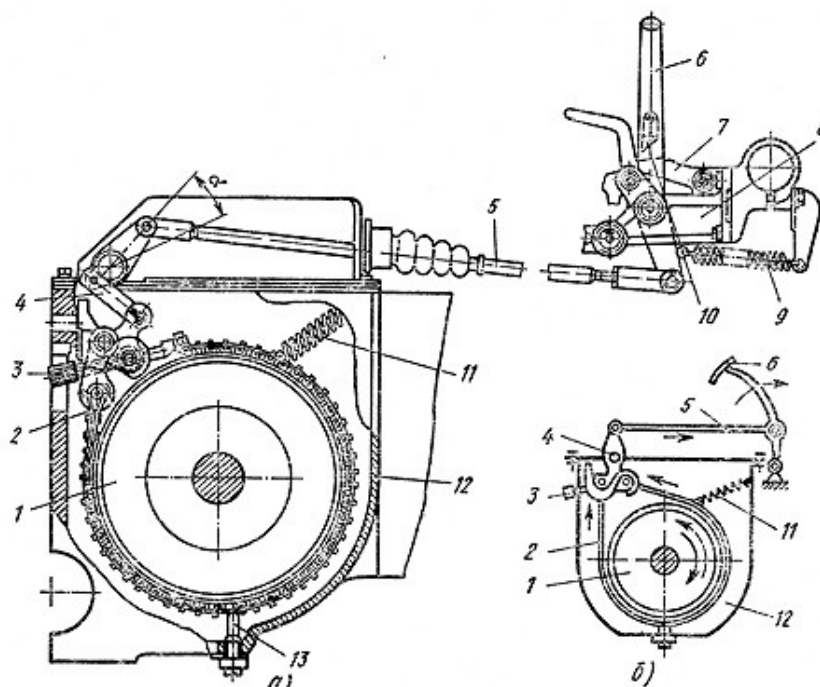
Плавающий тормоз с механизмом управления гусеничным трактором: а — устройство, б —
